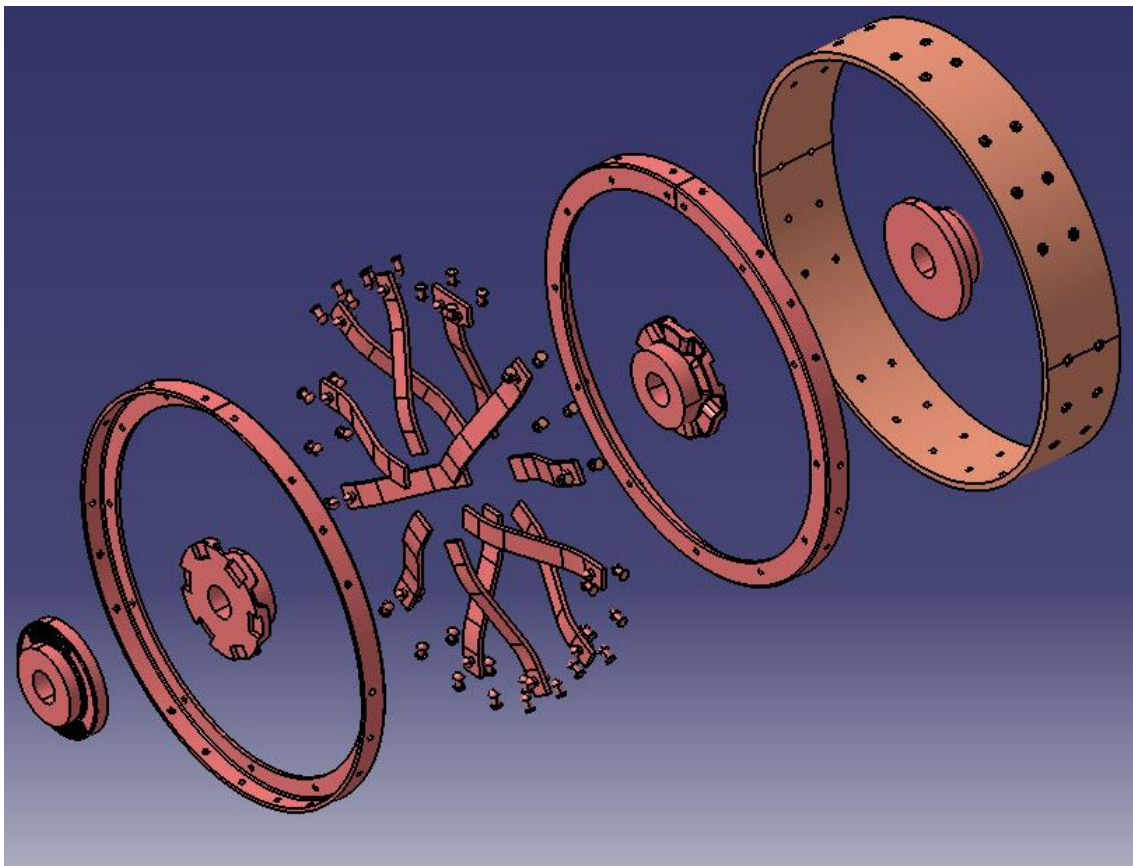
Conjunto rueda delantera con sus piezas explosionadas
